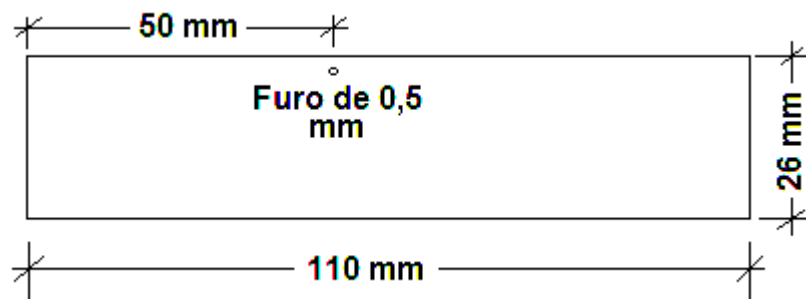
Esquema da furação das chapas de aço para execução da amostra de ensaio de rectificação profunda
